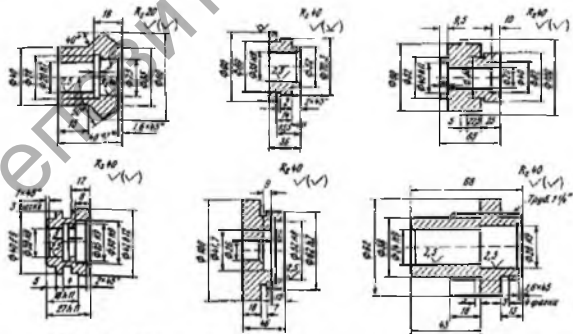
Типовые детали, получаемые на токарно-револьверных станках
